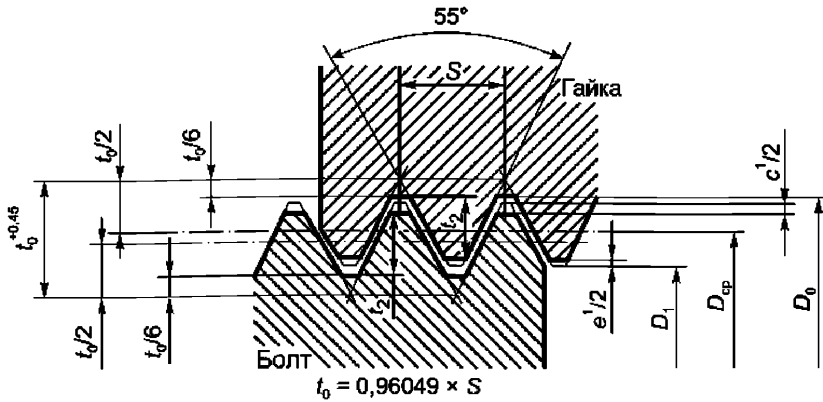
Схема внутренней резьбы резьбового кольца
